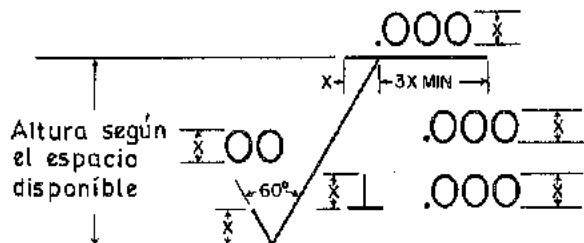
Proporciones recomendadas del símbolo de superficie (Micrometrical Manufacturing Co.)
